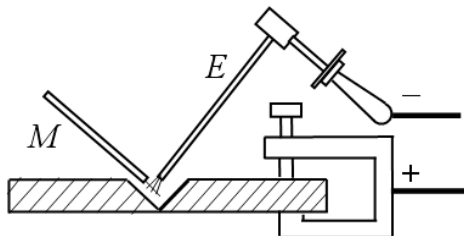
Soudage par le méthode de N. Benardos
